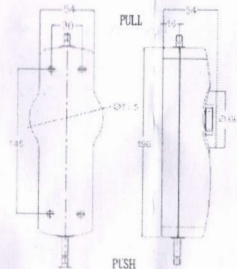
Габаритные и присоединительные размеры динамометра с цифровым отсчетным устройством ДЦ
